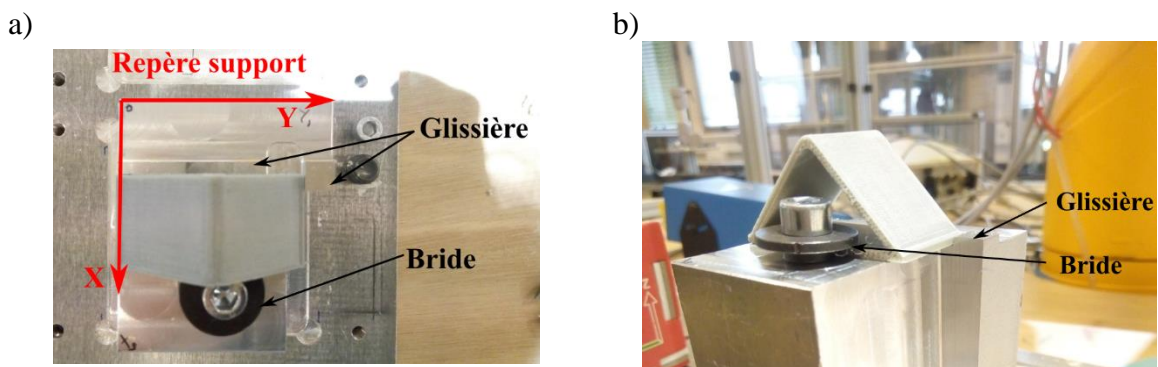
Exemple de support de pièces à imprimer a) Vue du dessus b) Vue de face
